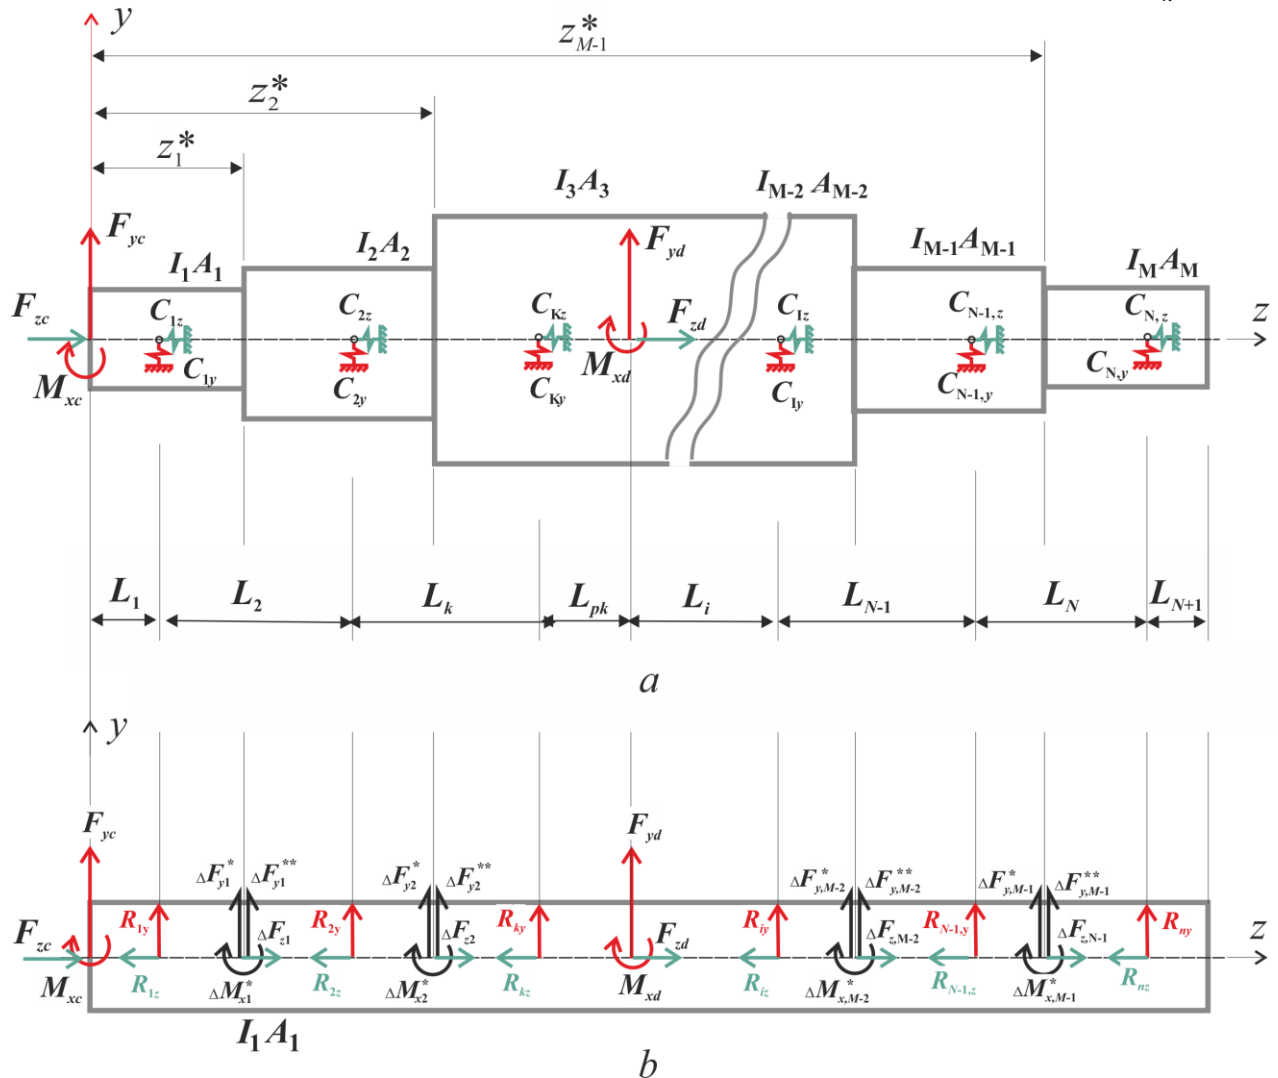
Розрахункова схема багато опорного ступінчатого шпиндельного валу
